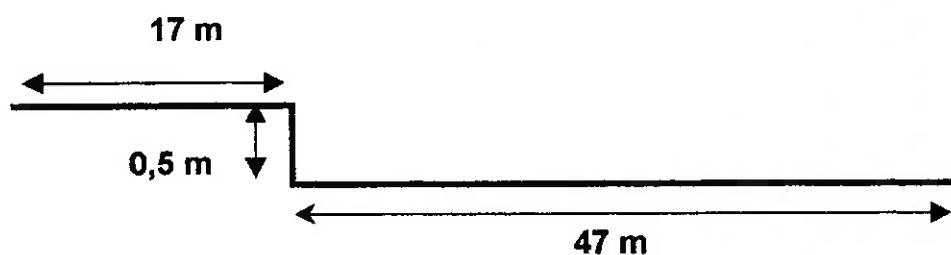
Desenho esquemático com as dimensões do transportador contínuo.
